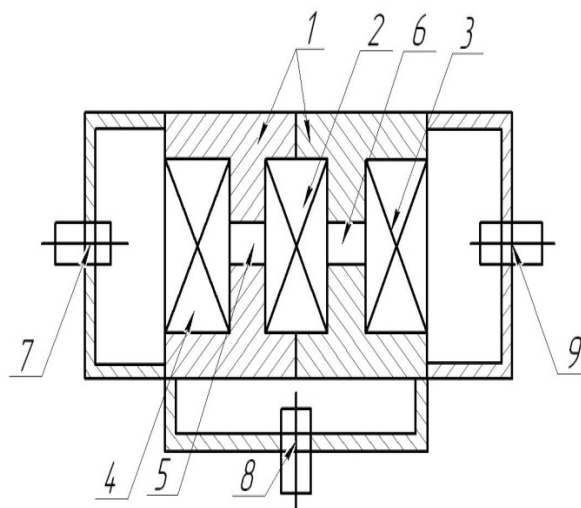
Общий вид ультразвукового датчика: 1 – корпус; 2 – излучатель; 3, 4 – приемники; 5, 6 – рабочие полости; 7, 8, 9 – электроразъемы
